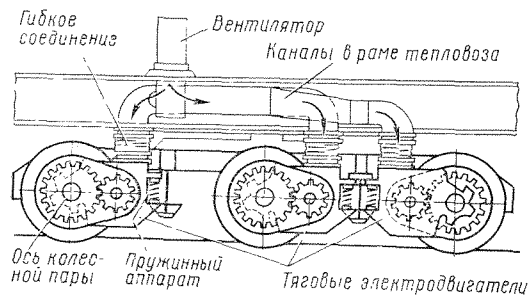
Схема установки и охлаждения тяговых электродвигателей
